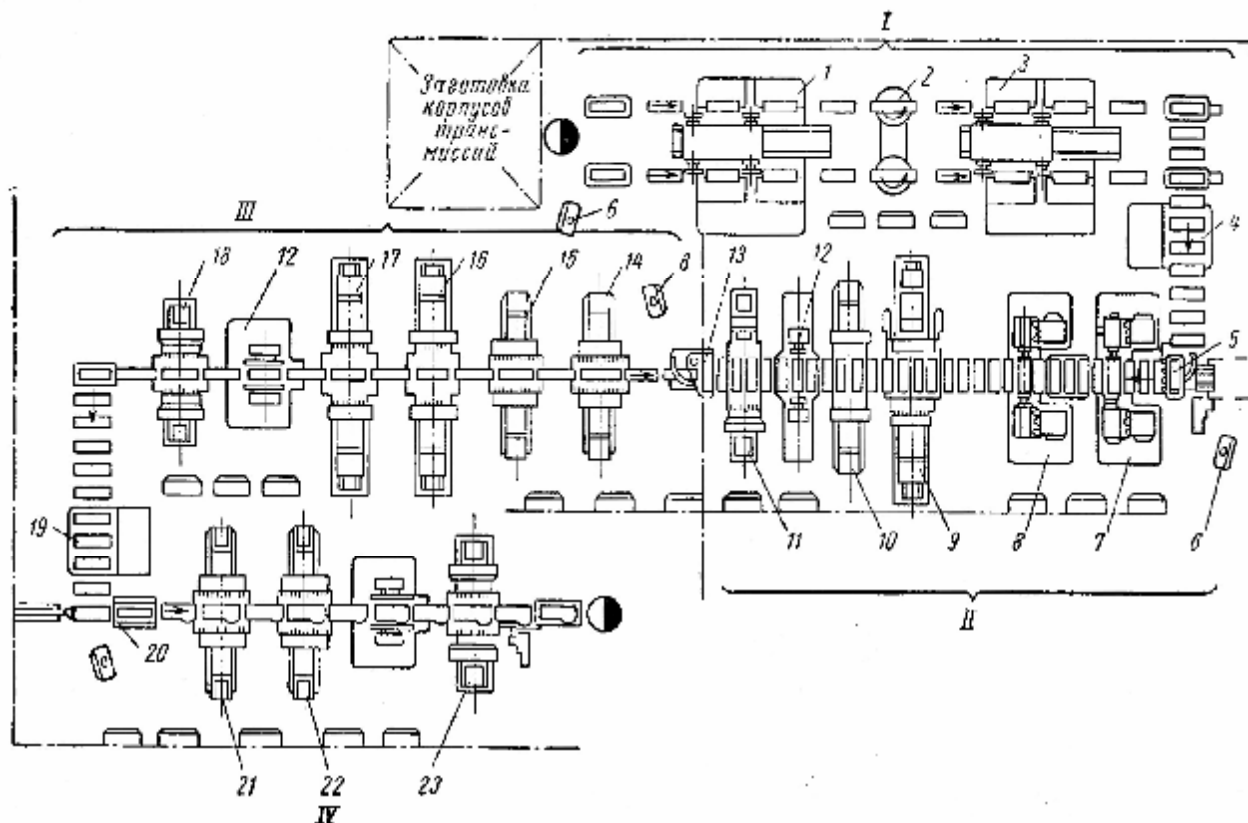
Схема автоматической линии для обработки корпуса трансмиссии трактора:
